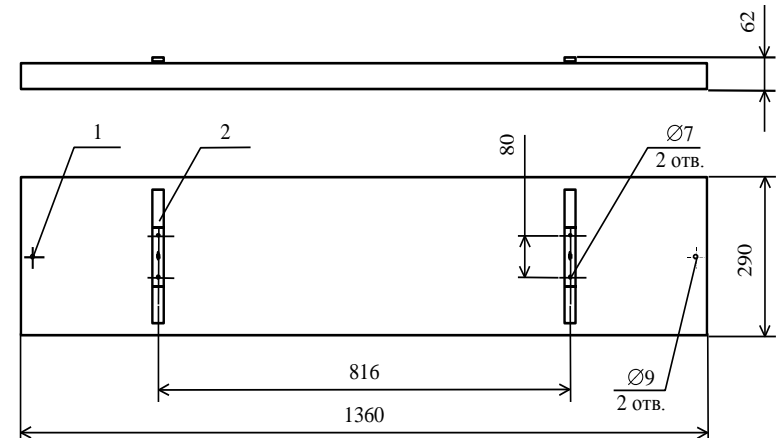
Габаритные и присоединительные размеры излучателя (в миллиметрах)
